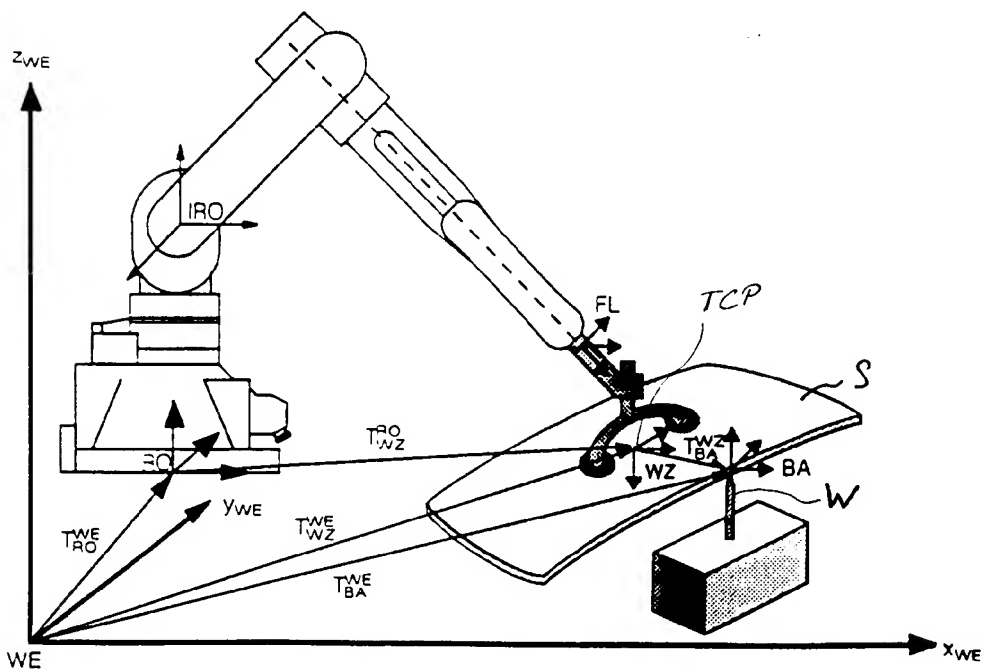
Führung des Werkstücks über ein ortsfestes Werkzeug
